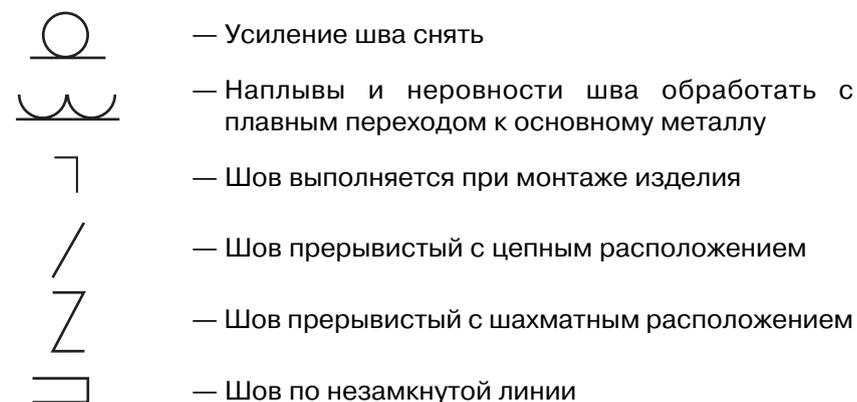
Специальные знаки условных обозначений сварных швов на чертежах (ГОСТ 2.312-72\*)
